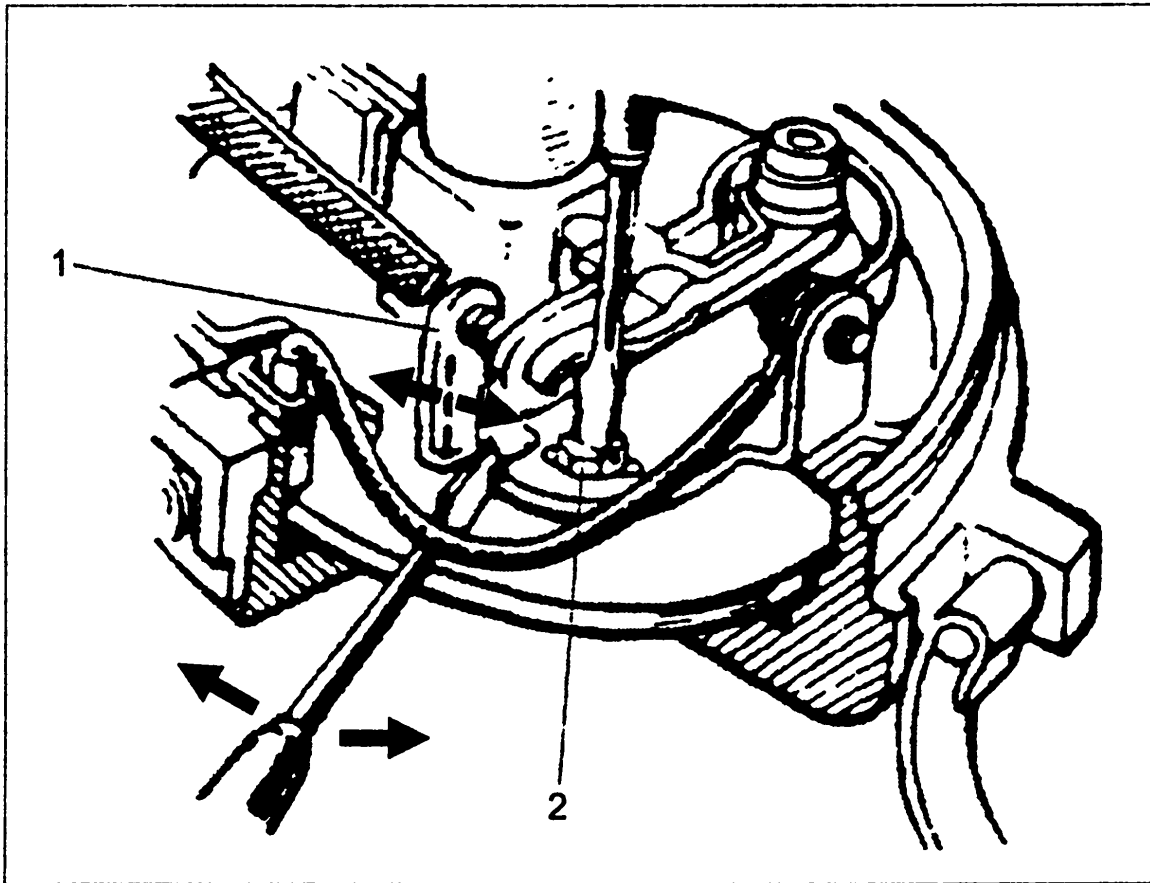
Регулировка зазора между контактами прерывателя зажигания автомобиля ВАЗ:
